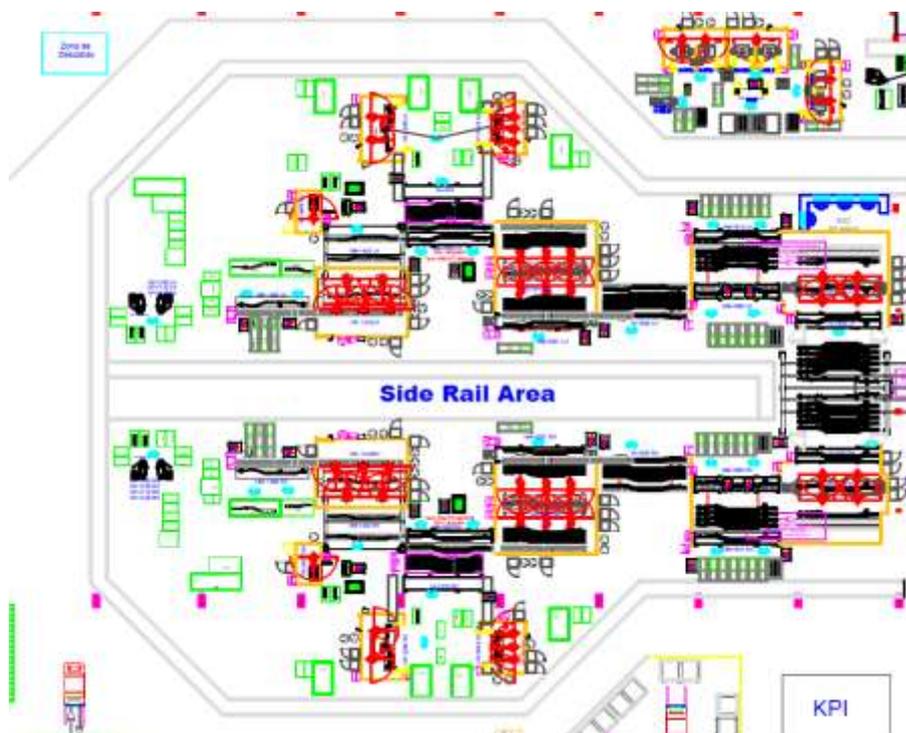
Lay out de la soldadura de Side Rails de Toyota. Provisto por Metalsa.
